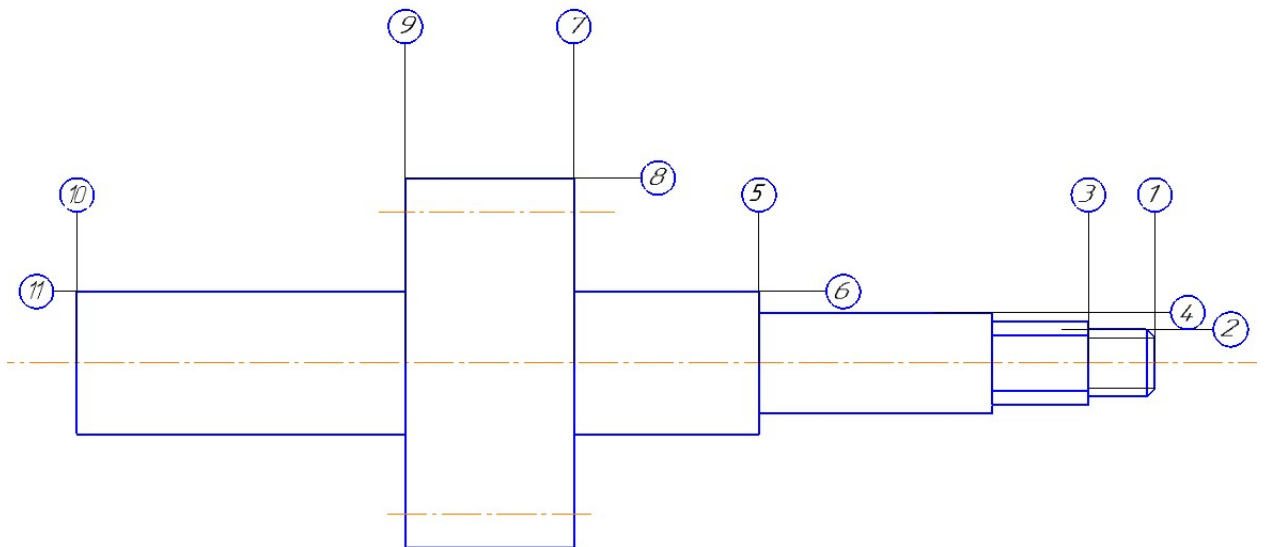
Схема нумерації поверхонь шестерні.
